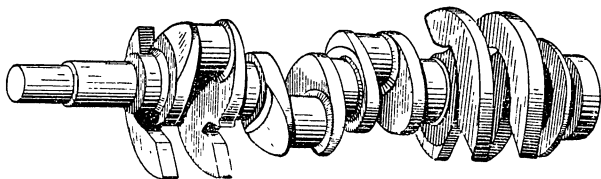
Коленчатый вал дизеля ЯАЗ-204
